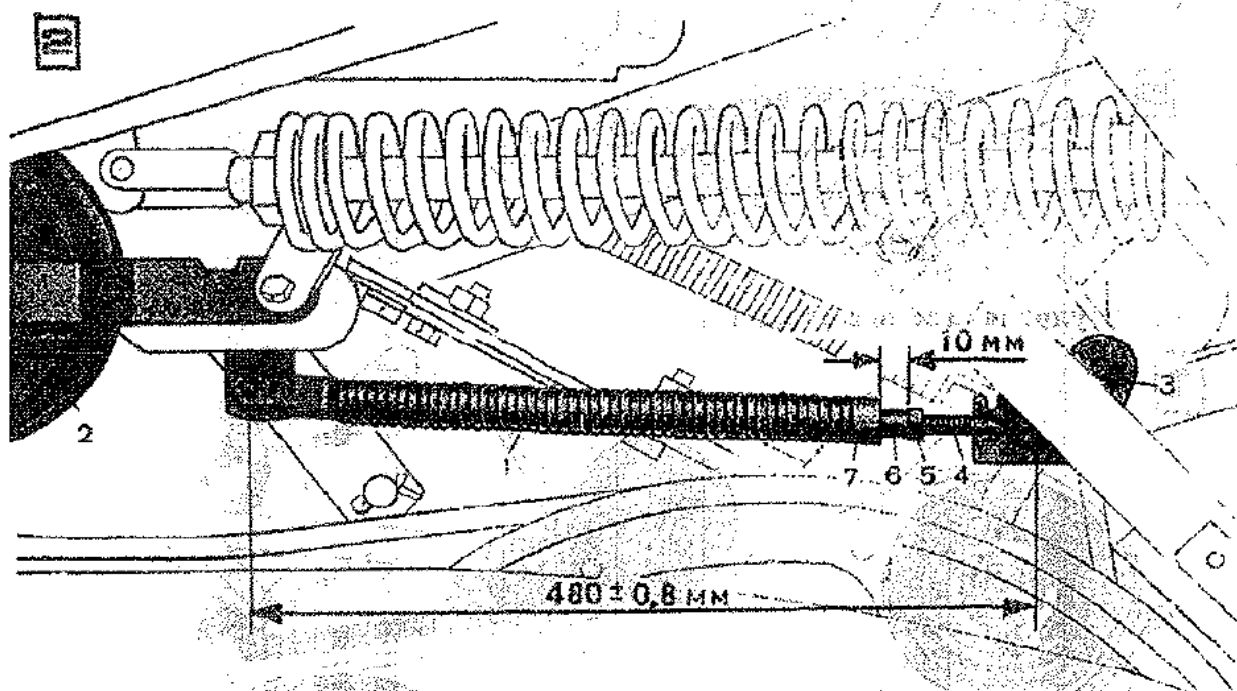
Схема механизма включения привода: 1 – пружина; 2 – шкив; 3 – кривошип; 4 – тяга; 5 – контргайка; 6 – ось; 7 – пробка
